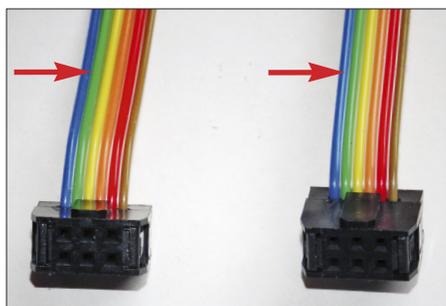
Beim fertigen Steuerkabel muss in dieser Ansicht die Farbreihenfolge der Kabeladern bei beiden Steckern identisch sein.
